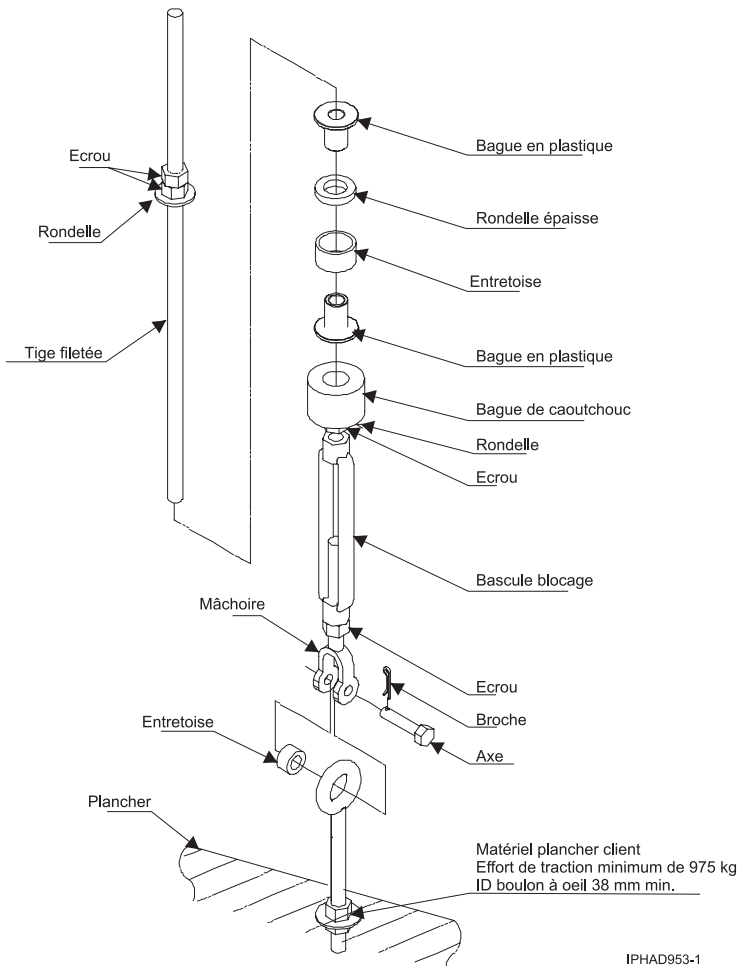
Matériel d'ancrage d'assemblage de lanterne de tendeur pour un faux plancher de 304,8 mm à 558,8 mm (44P3000)
